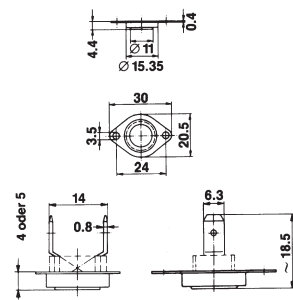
Flansch mit beidseitiger Befestigung abgesetzt
